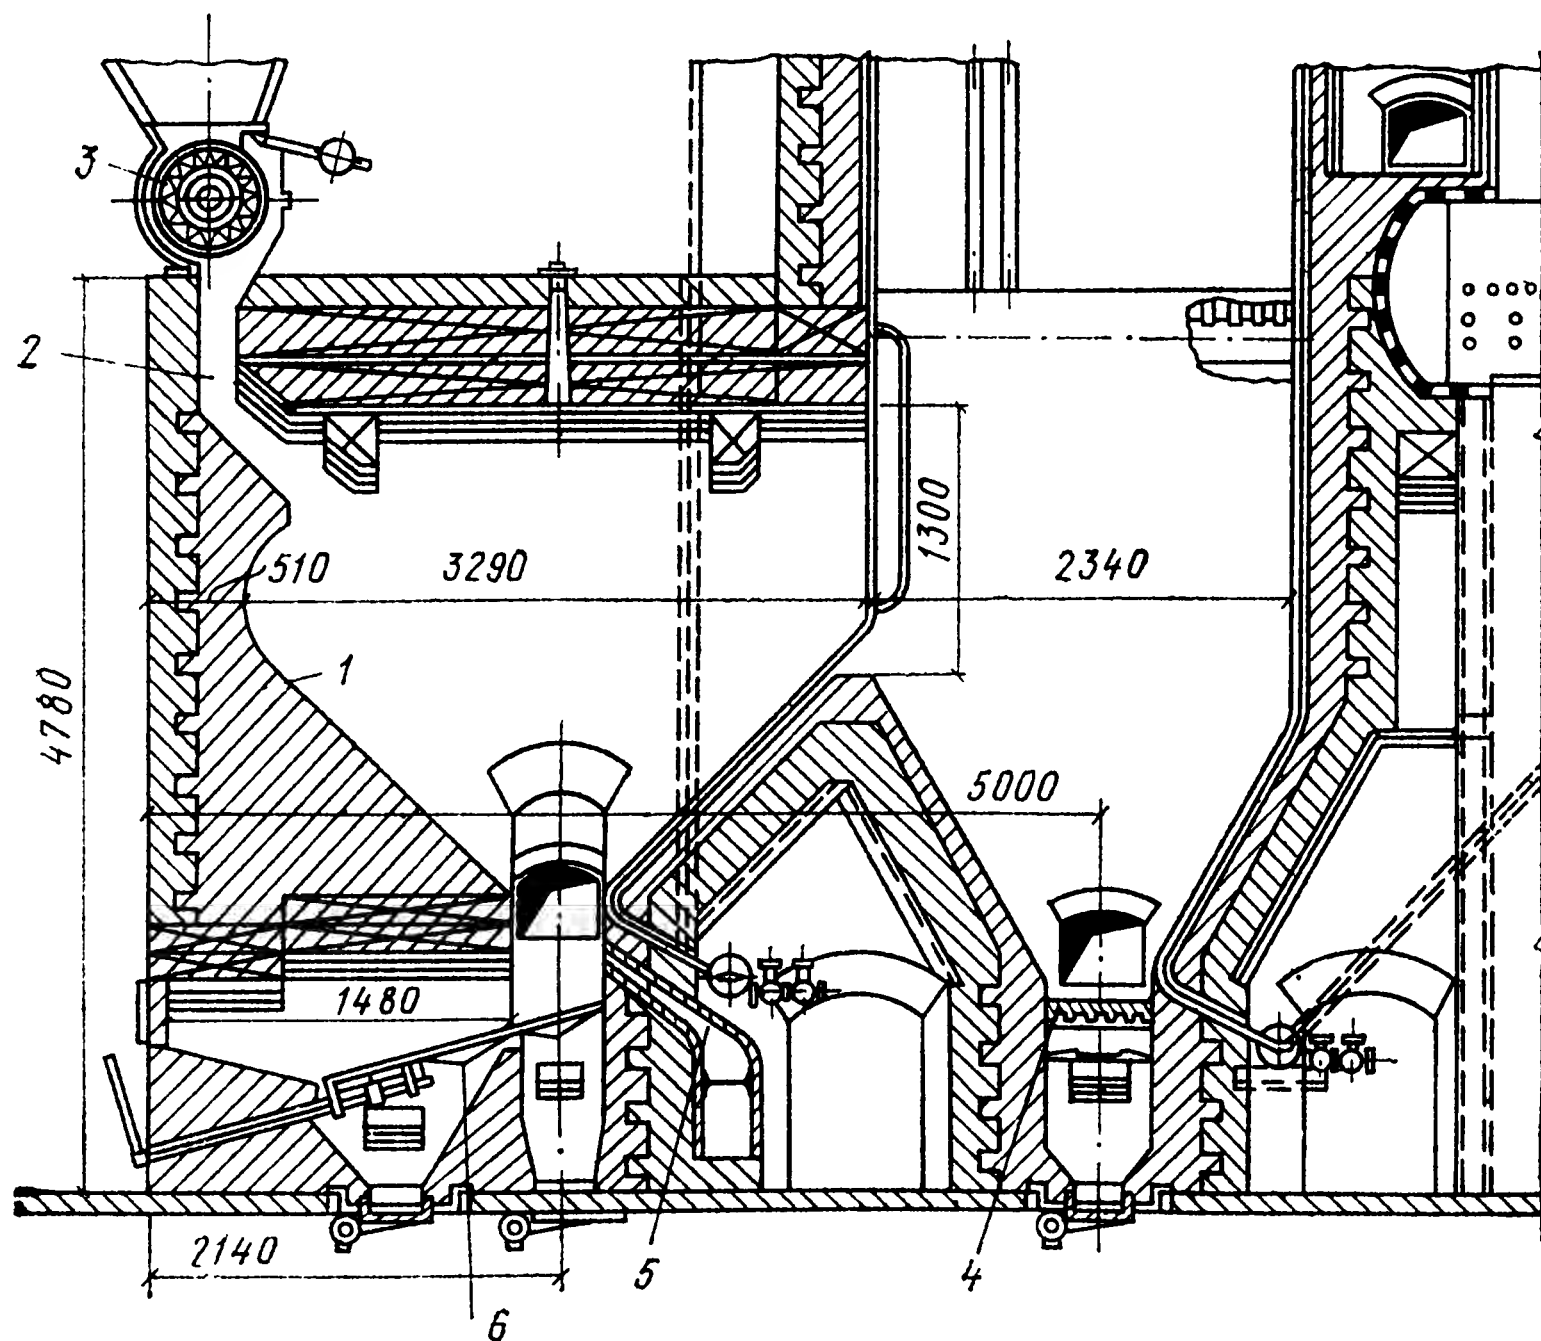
Топка для сжигания фрезерного торфа системы Шершнева
